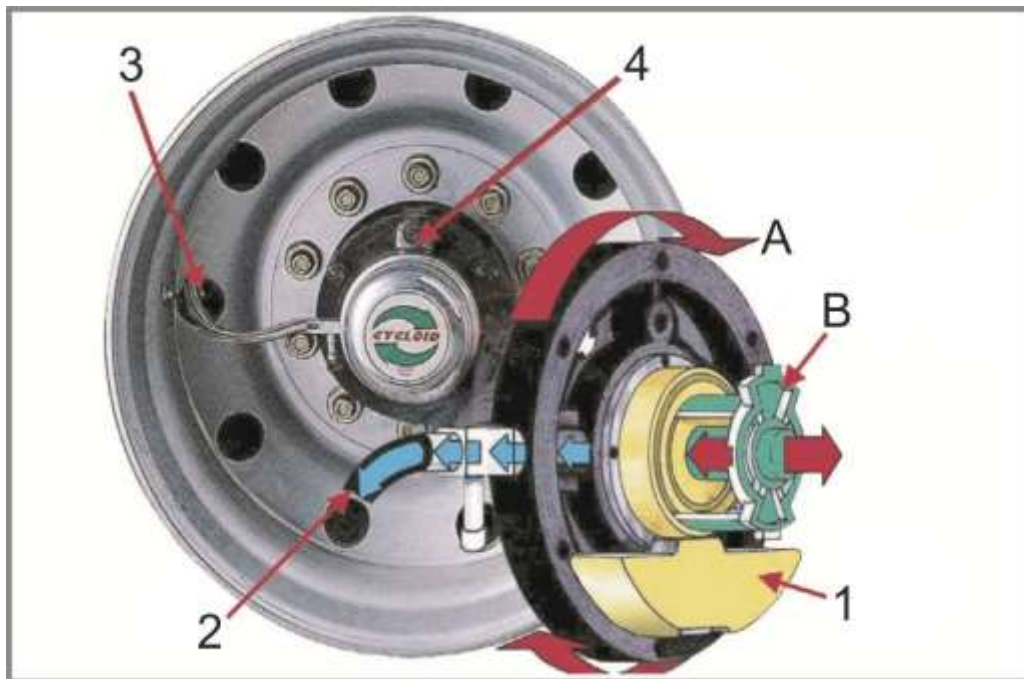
Насос фірми Cycloid постійного підкачування шин: 1 – нерухома противага і куліса; 2 – вихід повітря; 3 – з'єднання з вентилям шини; 4 – кріплення до маточини; А – корпус насоса обертається разом з колесом; В – поршень, обертаючись, рухається вперед-назад вздовж прорізів куліси
